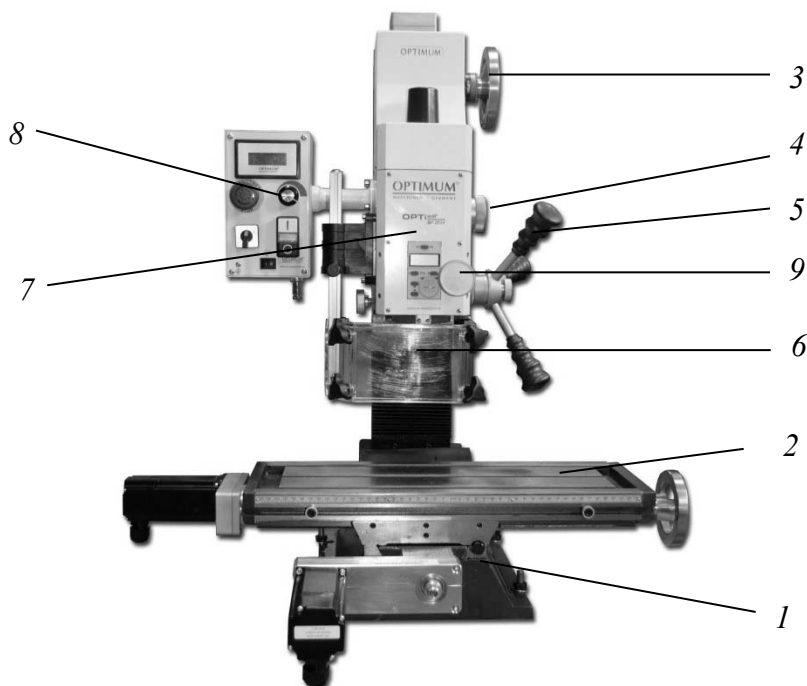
Общий вид фрезерного станка модели Optimum BF20 Vario
